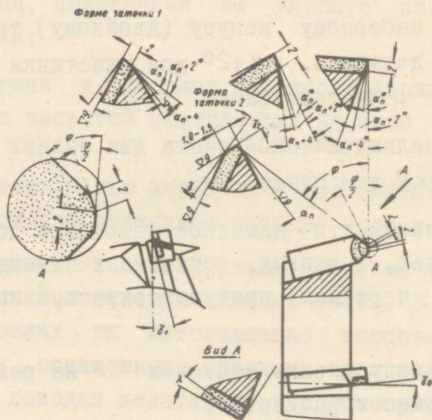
Углы заточки торцовой фрезы в сборе под алмазную обработку.
